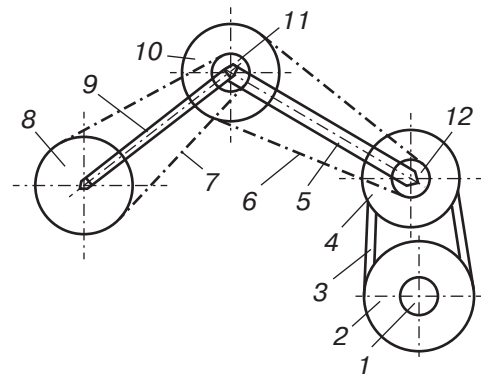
Кінематична схема механічного приводу мотовила:
